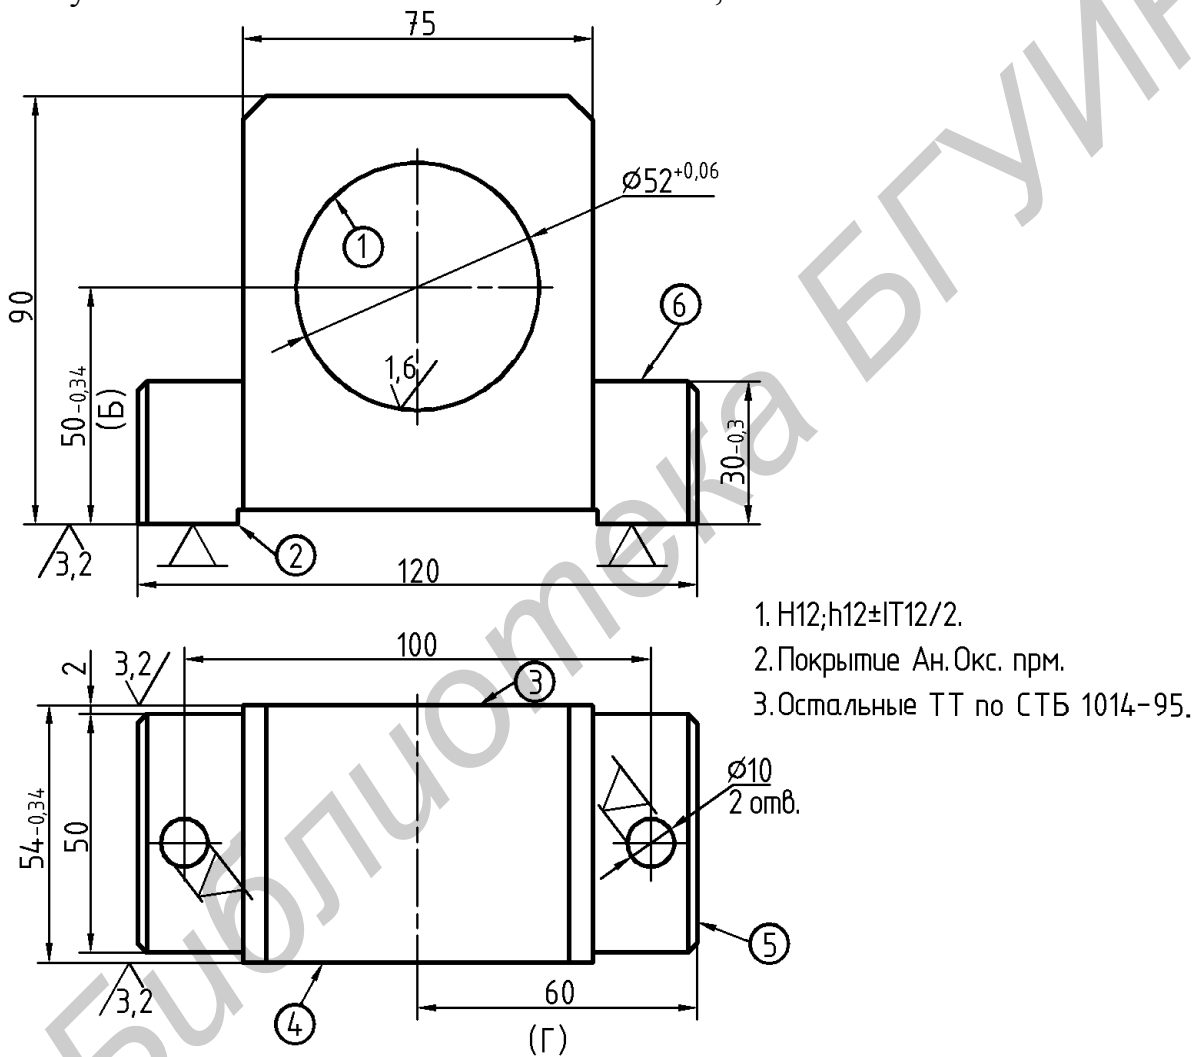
Корпус подшипника: чертеж и схема установки при обработке отверстия $\varnothing 52^{+0,06}$ мм
